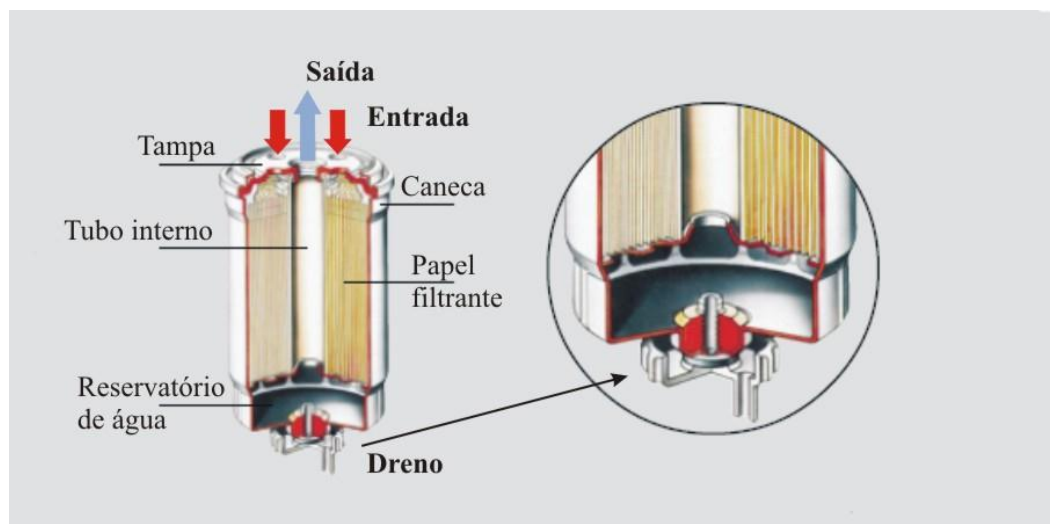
Filtro de combustível para motores diesel e seus componentes.
